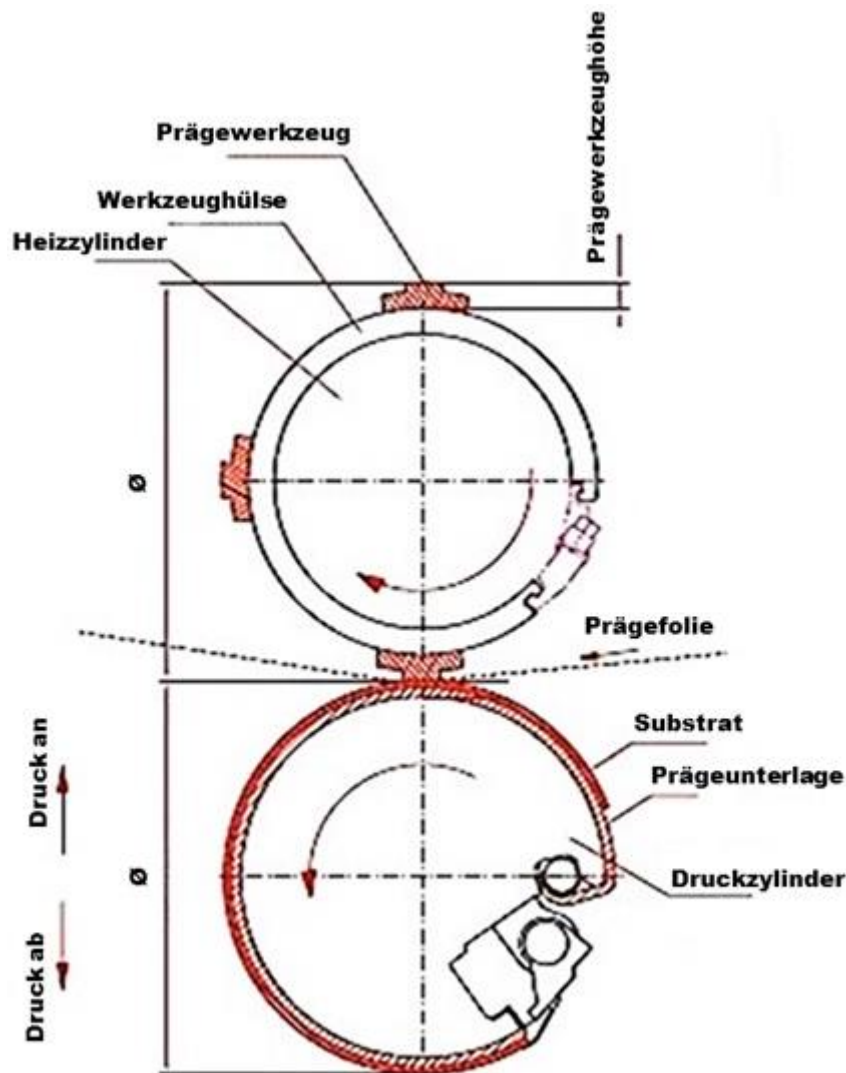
Skizze einer Prägefoliendruckmaschine „Rund auf Rund“. Sowohl das Prägewerkzeug als auch die Gegendruckform/Druckzylinder sind rund. Bildquelle: [ARB05].
